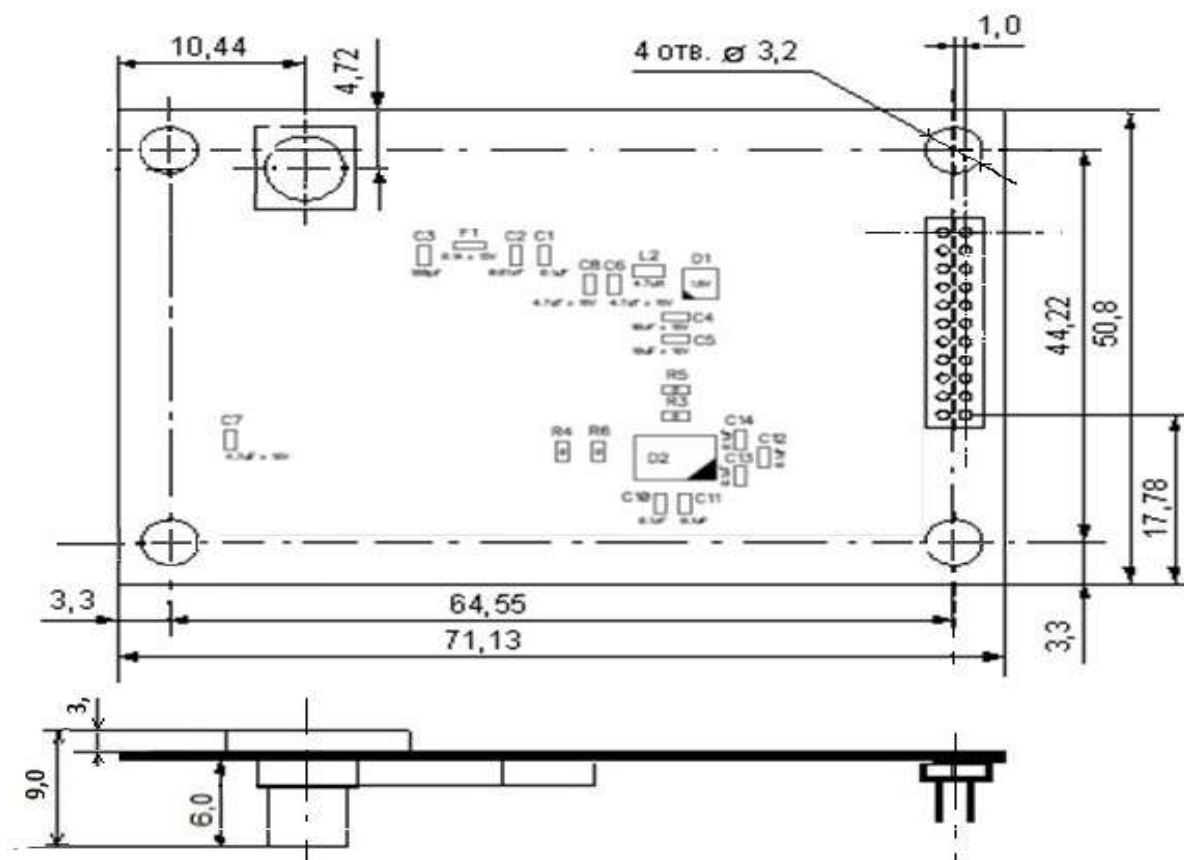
Сборочный чертёж аппаратуры ГАЛС-ПМ
